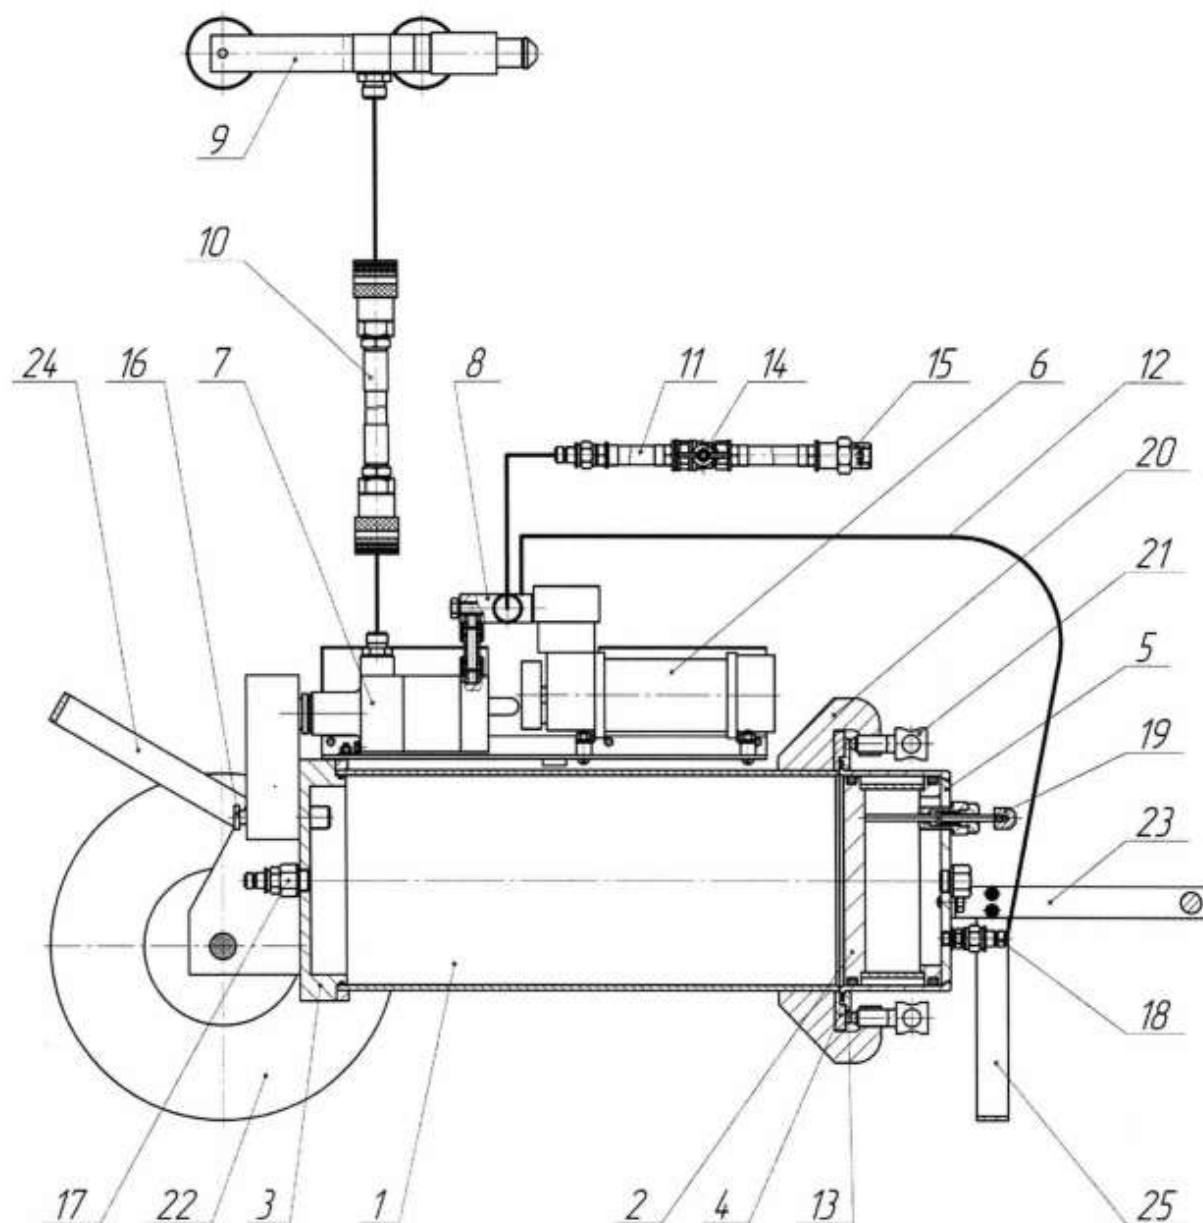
Патент № 2576080 - Установка для нагнетания смазки
